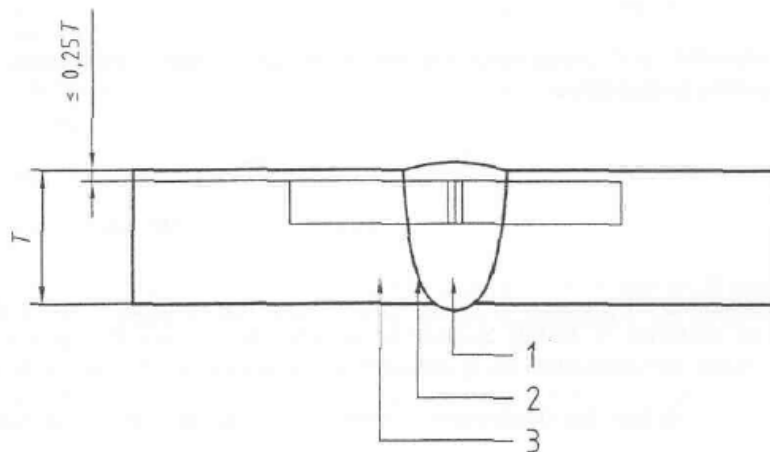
Местоположение образца металла сварного с V-образным надрезом по Шарпи.
